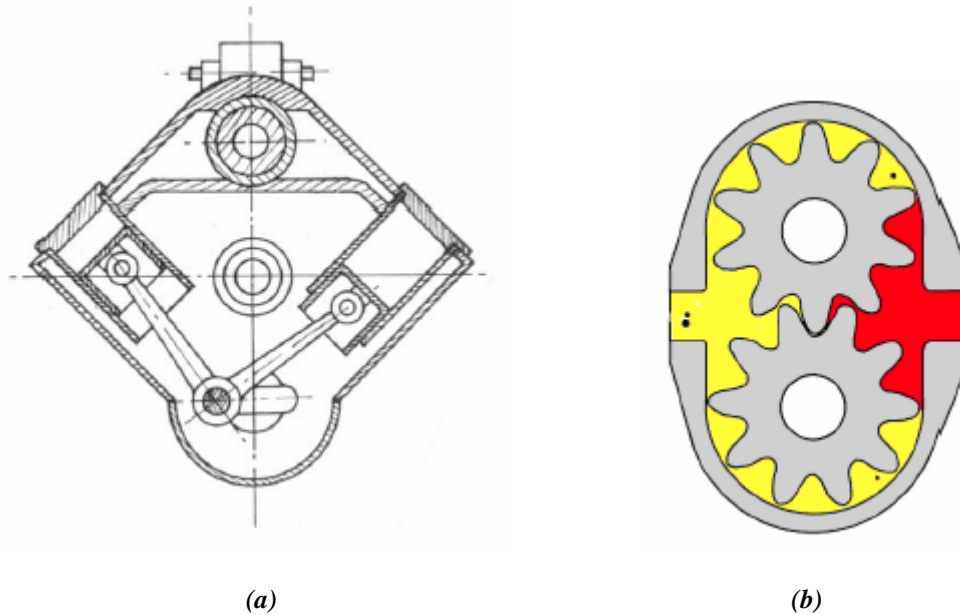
Motor neumático: (a) de pistones; (b) de engranes.
